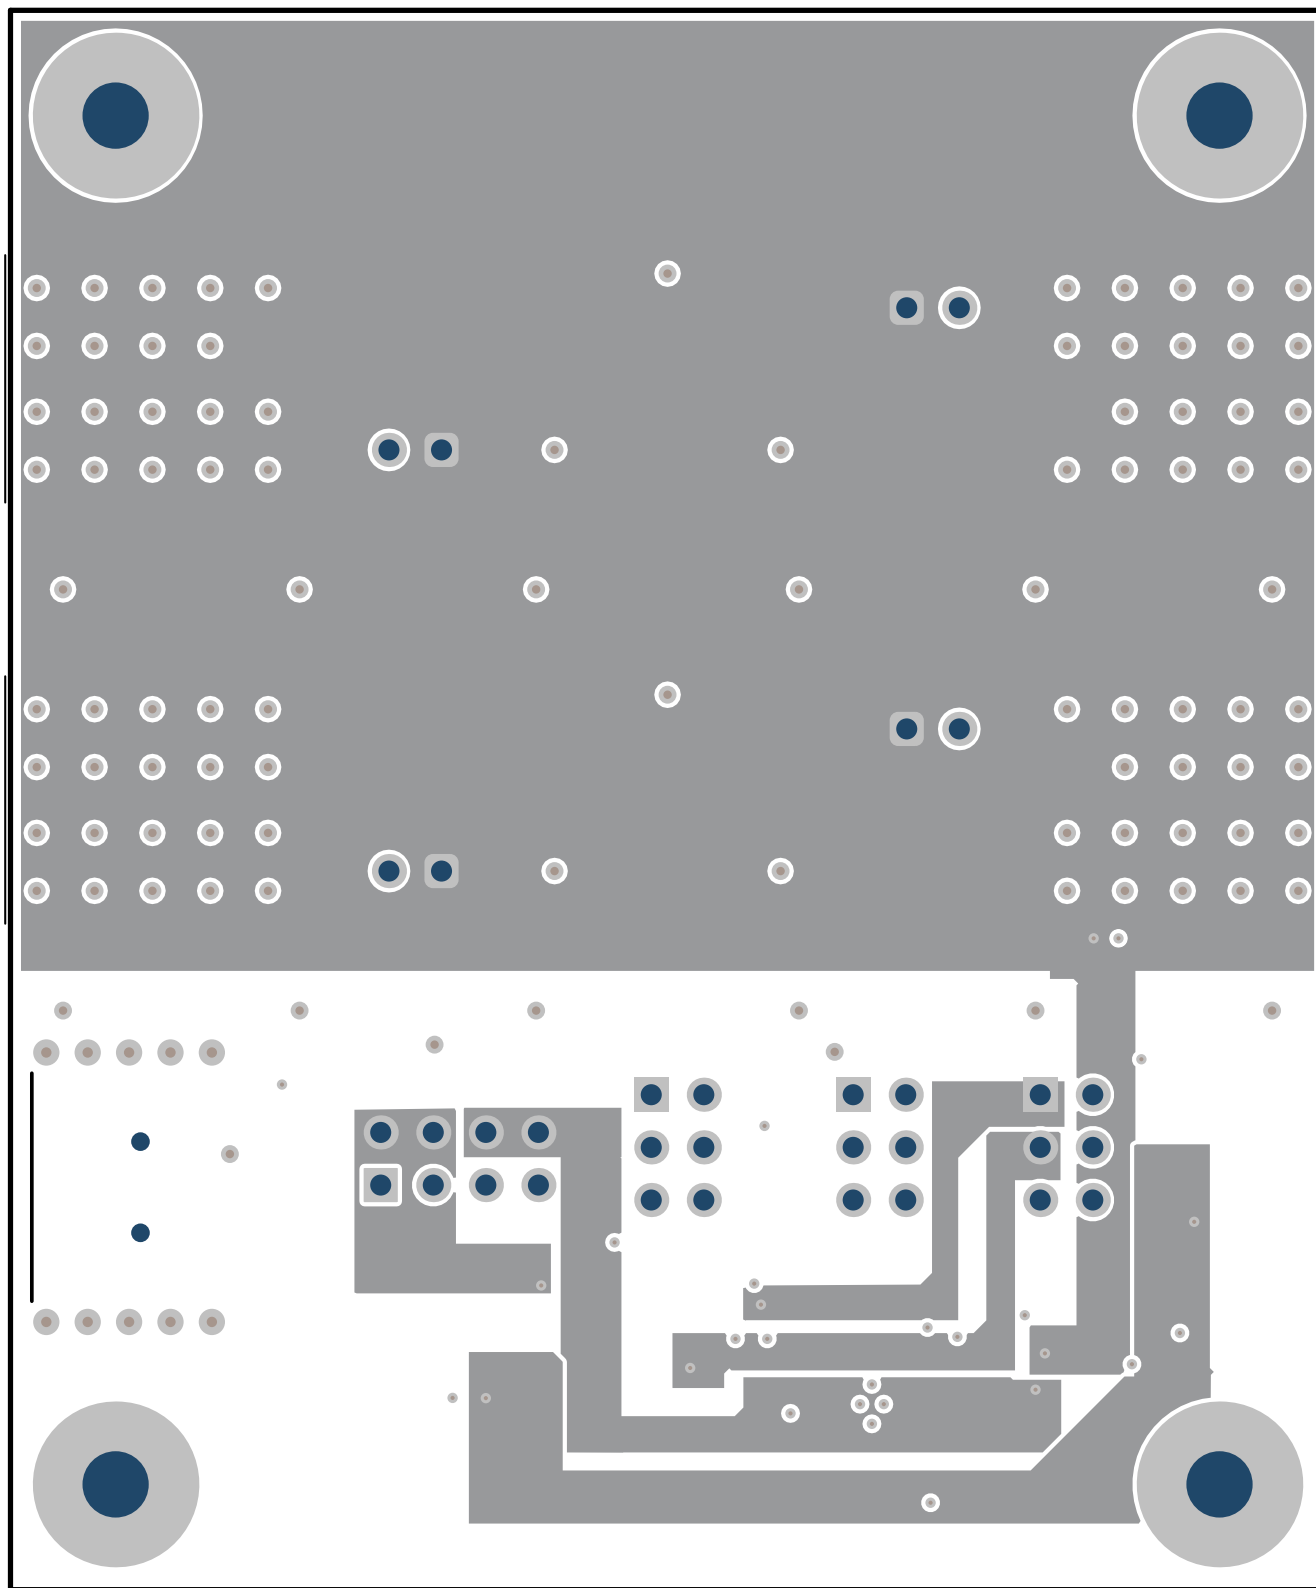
CDC6 EVM の PCB レイアウト例 — 電源層
